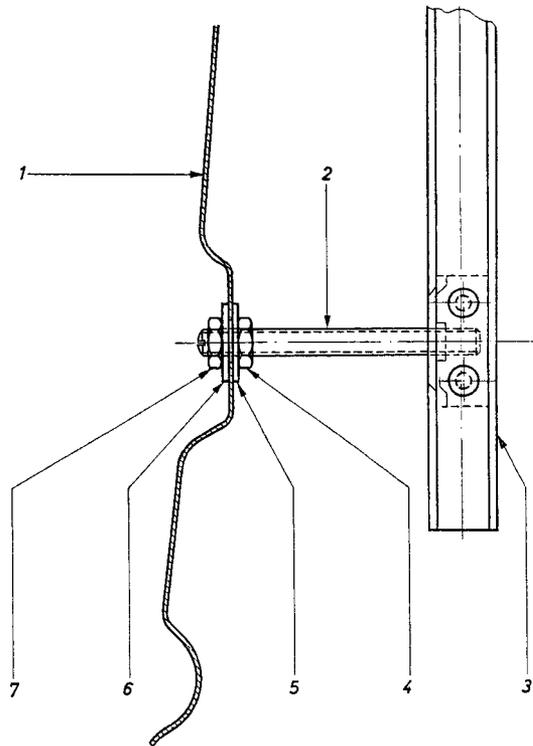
Anordnung des Gewindestiftes zum Korrigieren des Fensterrahmens
